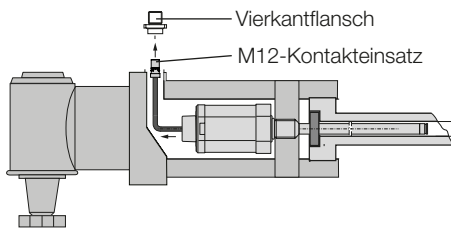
Stecksystem am Beispiel Einbau des Wegaufnehmers in einen Hydraulikzylinder
